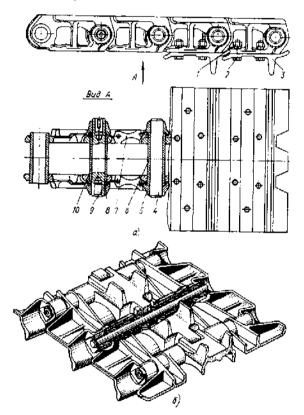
Гусеницы: а – цепная с башмаками; б – траковая; 1 – гайка с шайбой; 2 – болт крепления башмака; 3 – башмак с грунтозацепом; 4 – соединительный палец; 5, 7 – звенья; 6 – втулка звена; 8 – шайба замыкающего пальца; 9 – замыкающий палец; 10 – замыкающая втулка
